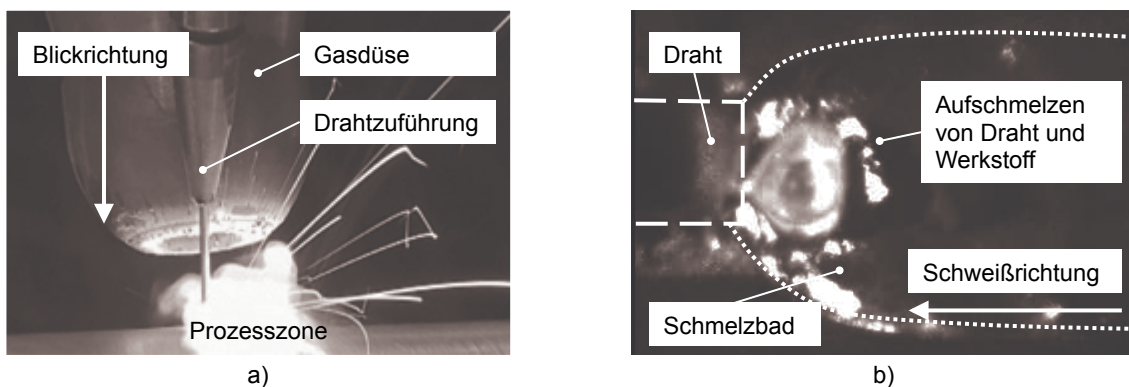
a) Zusatzdrahtzuführung im Schweißprozess mit eingezeichneter Blickrichtung für b) den Blick durch die Bearbeitungsoptik auf den Wechselwirkungsbereich beim Schweißprozess
